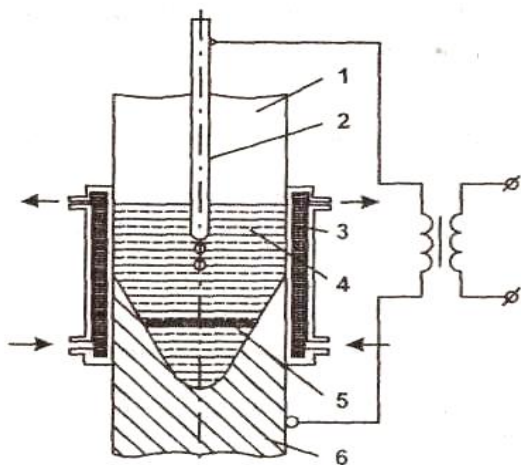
Схема процесса электрошлаковой сварки:
